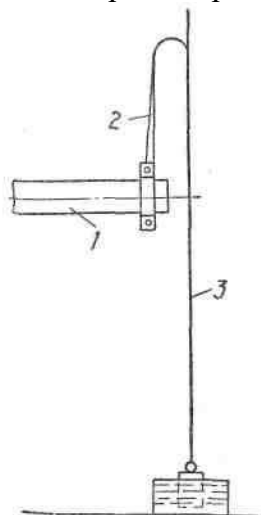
Проверка горизонтального положения вала при помощи стрелки и отвеса: 1— вал; 2 — стрелка; 3 — отвес
